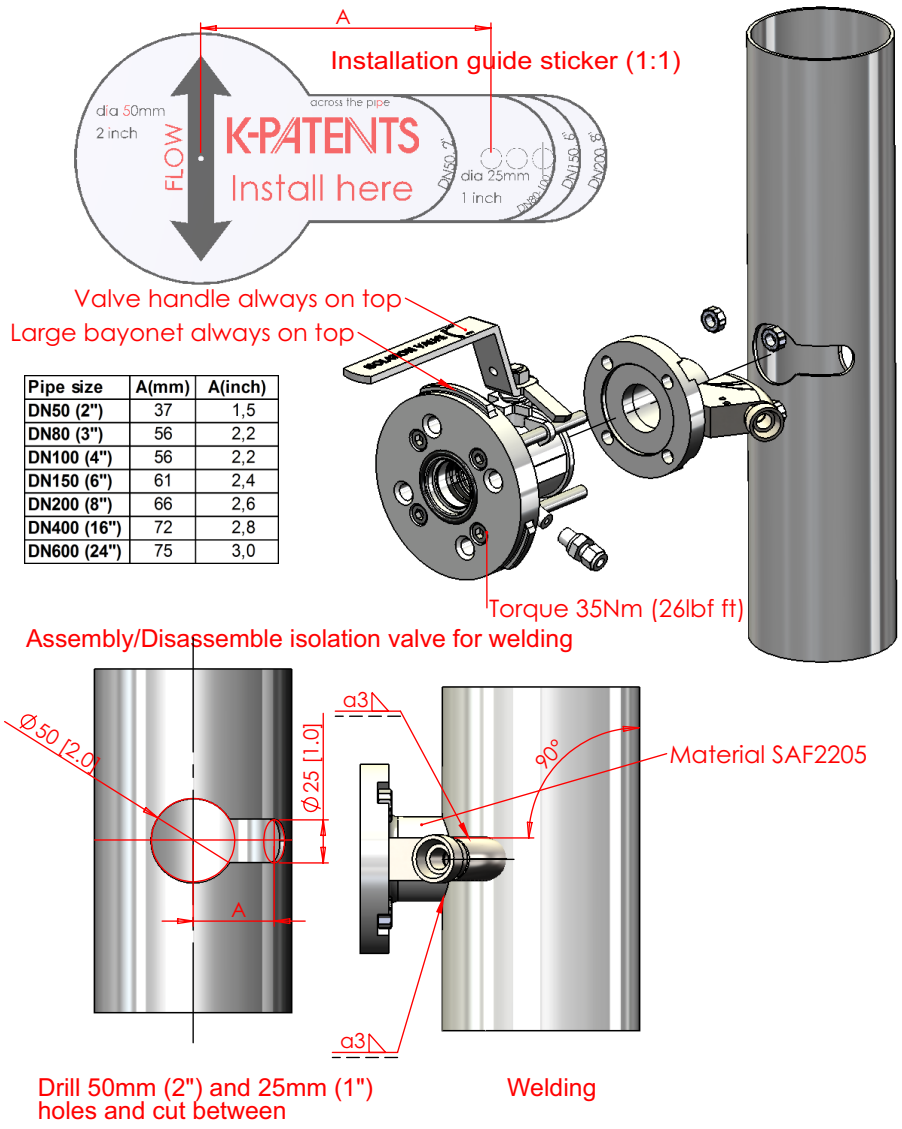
Soldadura de la válvula de aislamiento Safe-Drive™ a un tubo vertical
